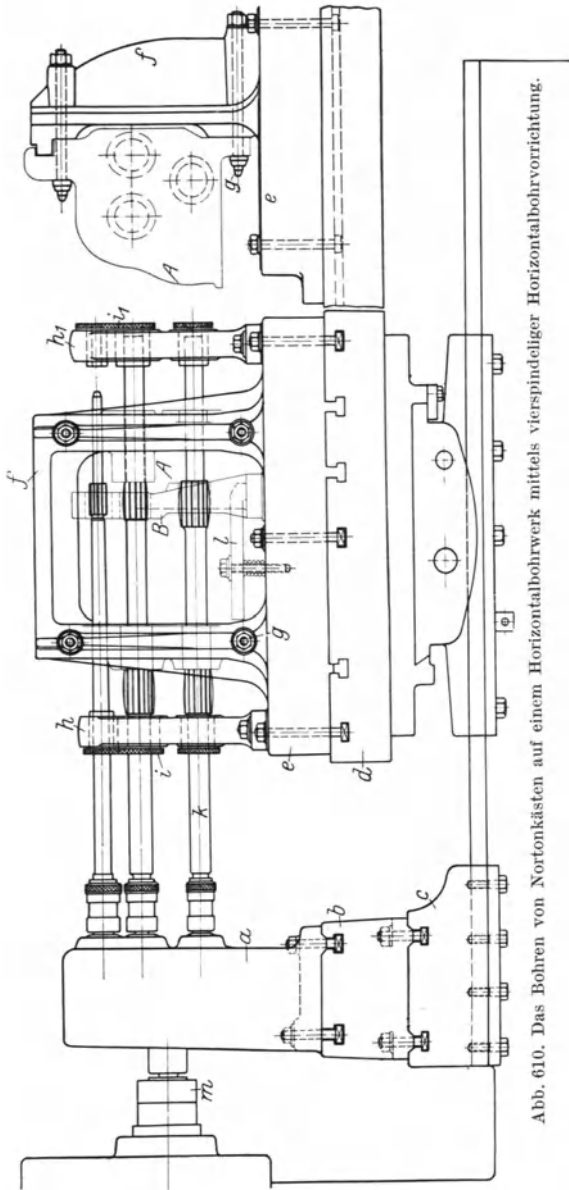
Das Bohren von Nortonkästen auf einem Horizontalbohrwerk mittels vierspindeliger Horizontalbohrvorrichtung.
